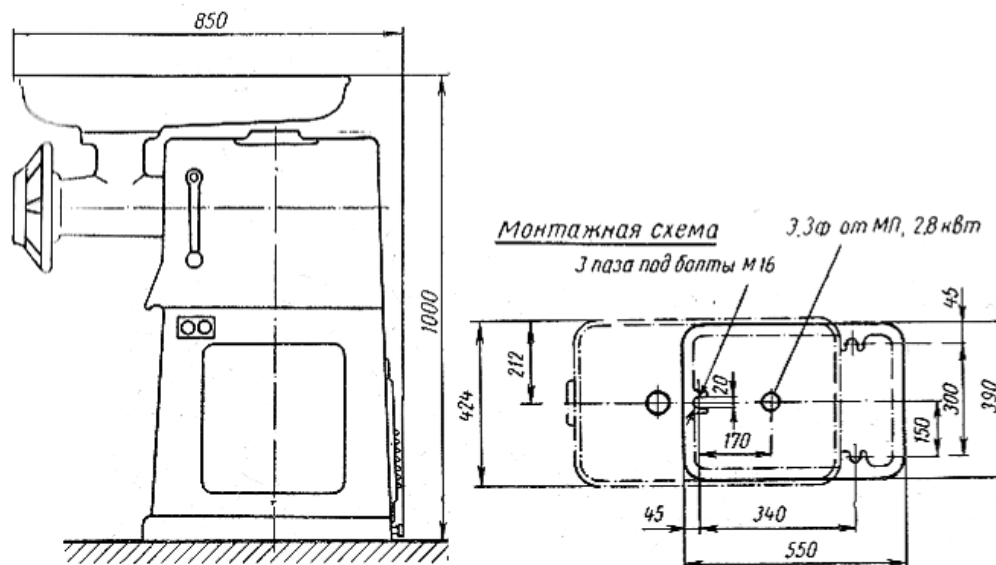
Установочный чертеж мясорубки типа М-4
